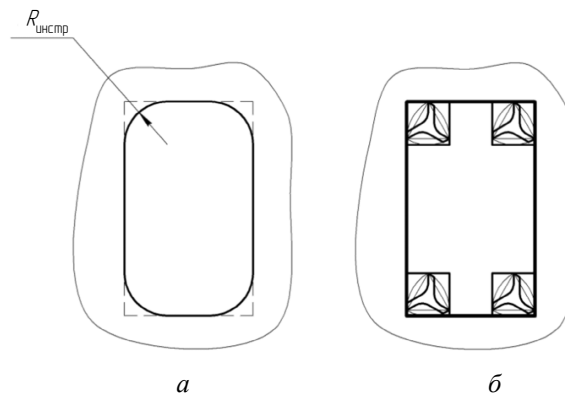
Технология обработки прямоугольных отверстий фрезой Уаттса: *a* – предварительная фрезерная обработка отверстия; *б* – окончательная обработка отверстия фрезой Уаттса
